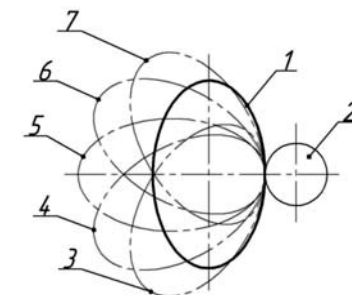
Положения заготовки некруглого зубчатого колеса относительно режущего инструмента: 1 – заготовка, 2 – режущий инструмент, 3, 4, 5, 6, 7 – позиции заготовки
